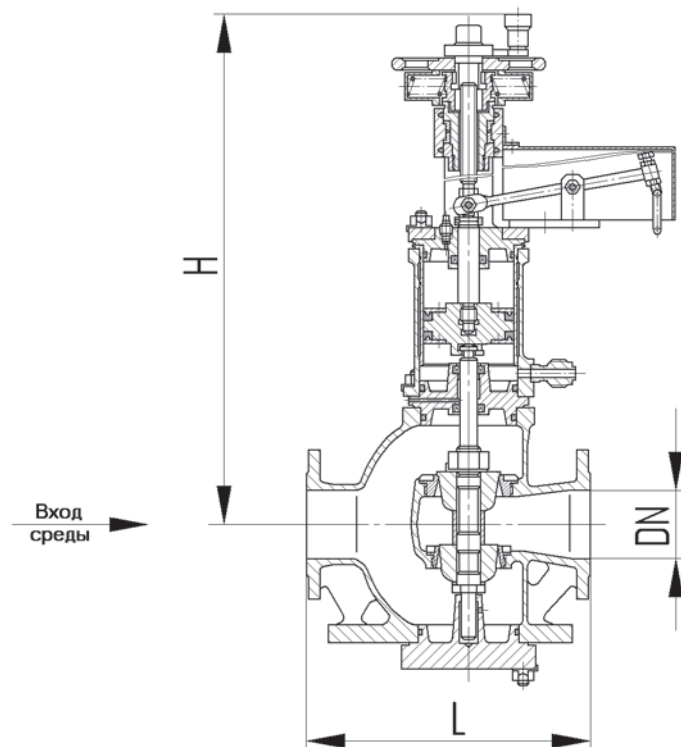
Клапан регулирующий проходной фланцевый
